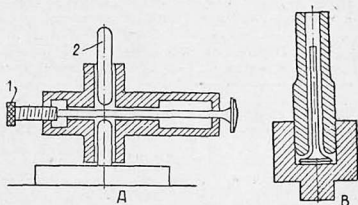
А — схема прибора для удлинения стержня клапана. В — матрица и пуансон для увеличения диаметра клапана
